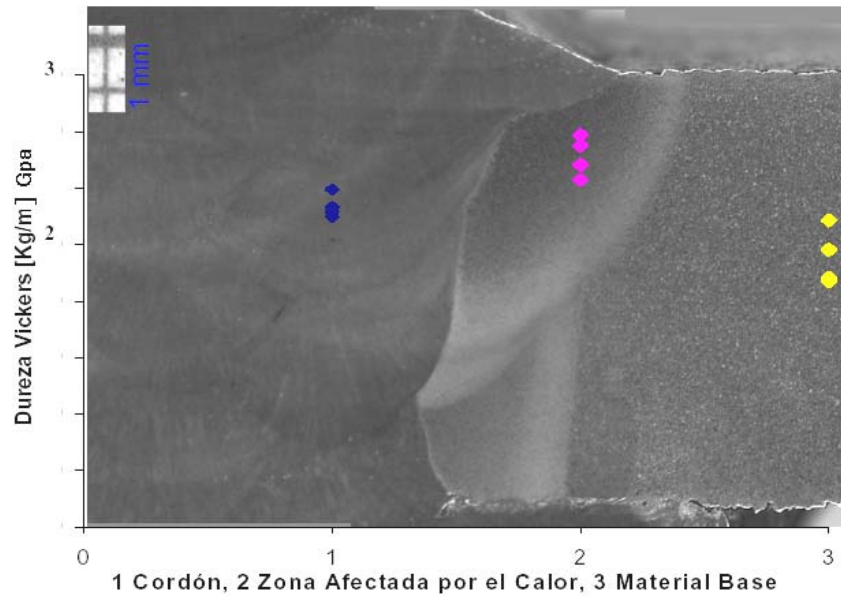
Perfil de dureza del conjunto Material Base- Cordón de Soldadura.
